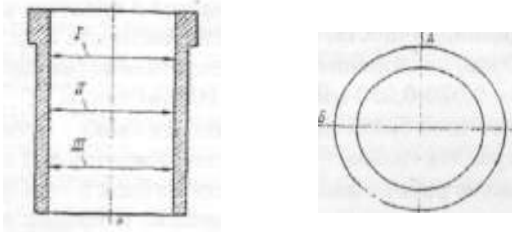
Схема обмера отверстия под поршень в гильзе цилиндра
